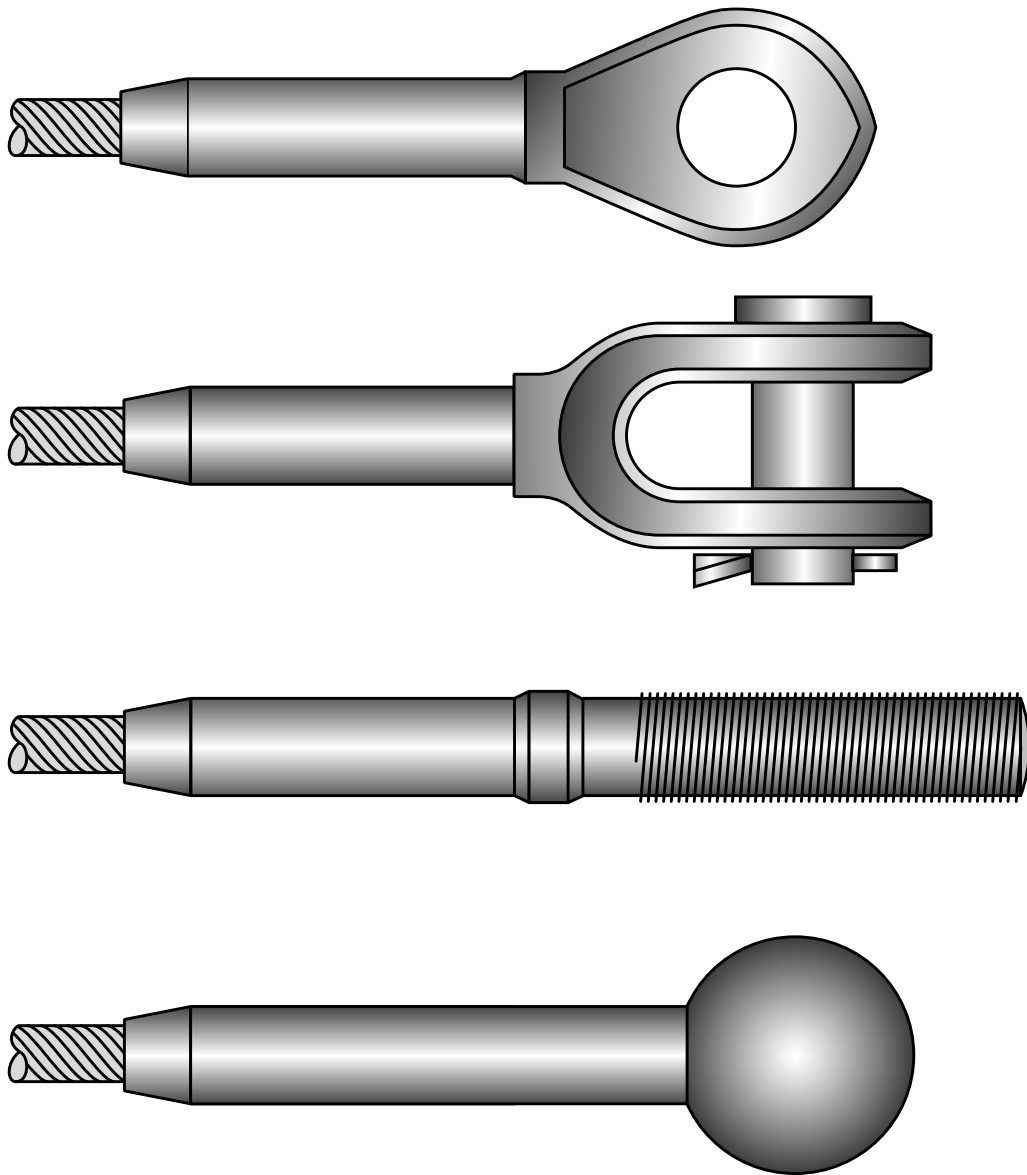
Ausführungsformen der Bolzenpreßverbindung
